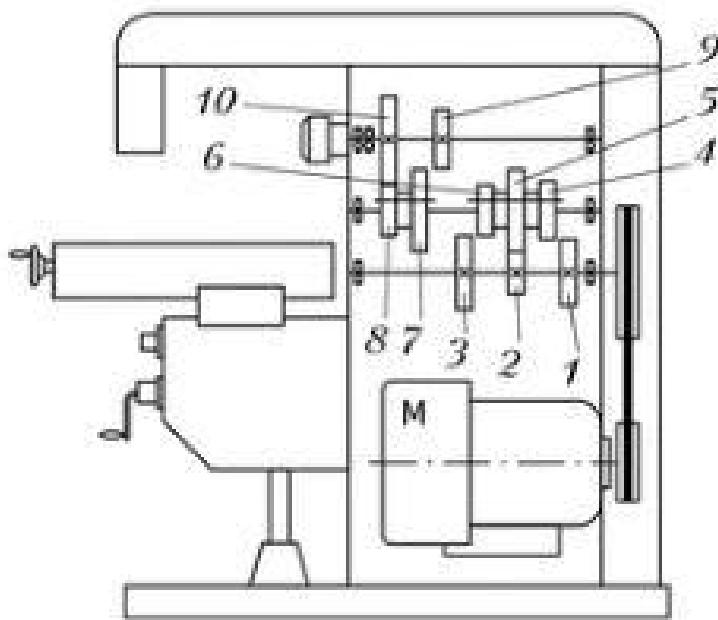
Упрощённая кинематическая схема фрезерного станка НГФ-110Ш:
